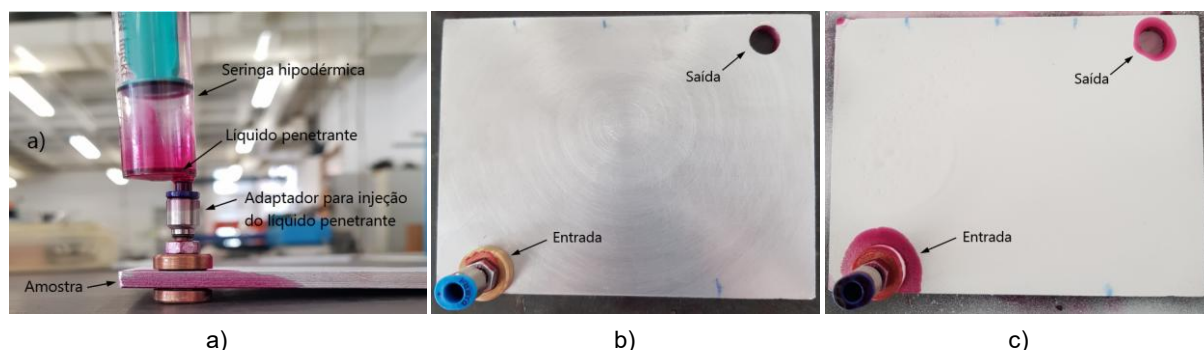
Teste com líquido penetrante; a) acessório para injeção de líquido; b) superfície após aplicação do líquido penetrante e limpeza; c) superfície do corpo de prova após aplicação do revelador: sem defeitos. Adaptado de [41].
